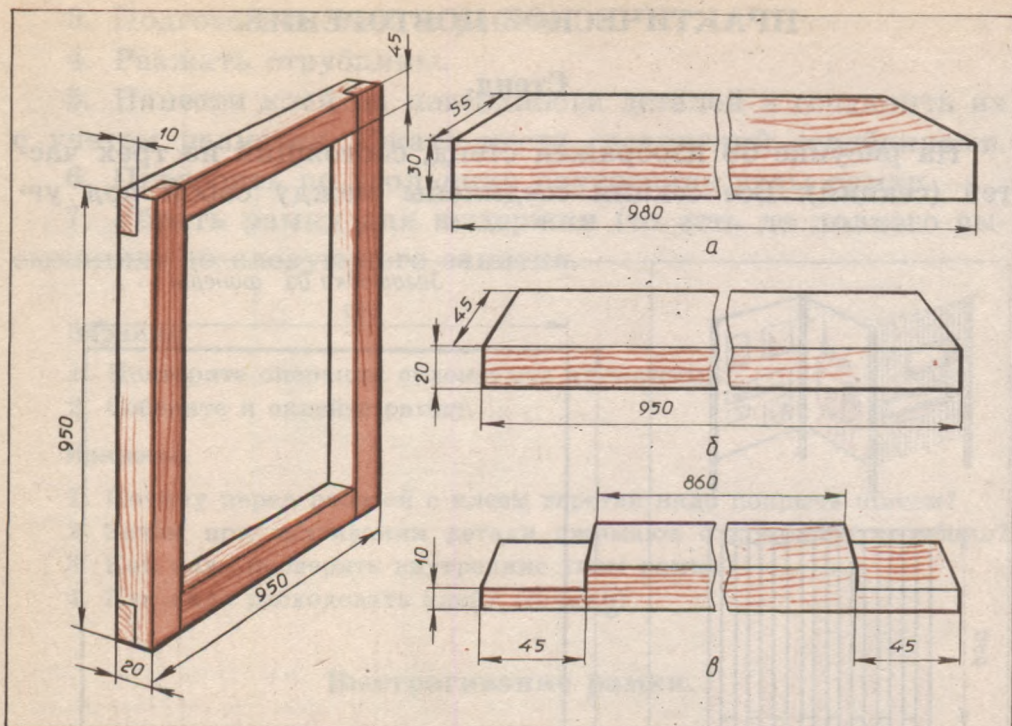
Подрамник для стенда: а — выпиленный брусок; б — выстроганный брусок; в — деталь с шипами вполдерева.
